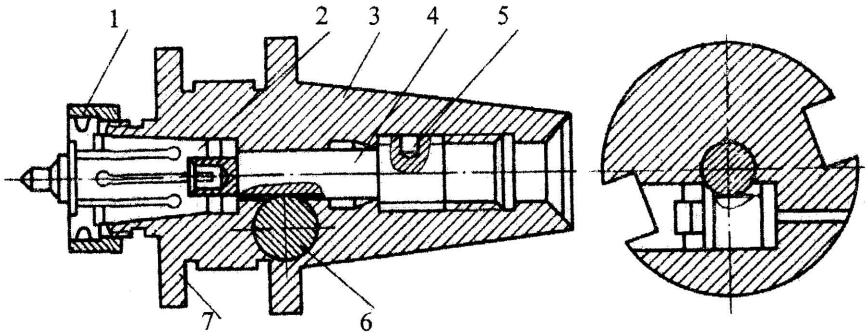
Патрон для крепления мелкого концевго инструмента
